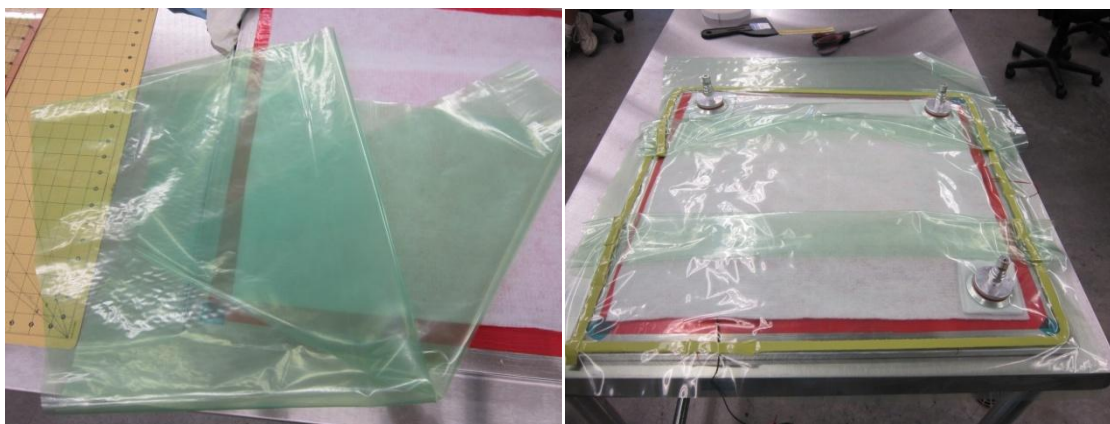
Material plástico que forma la última capa de la bolsa (izquierda) y conjunto de la bolsa de vacío terminada (derecha)
